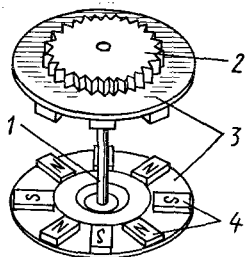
Ротор шагового двигателя со встроенными катушками:
